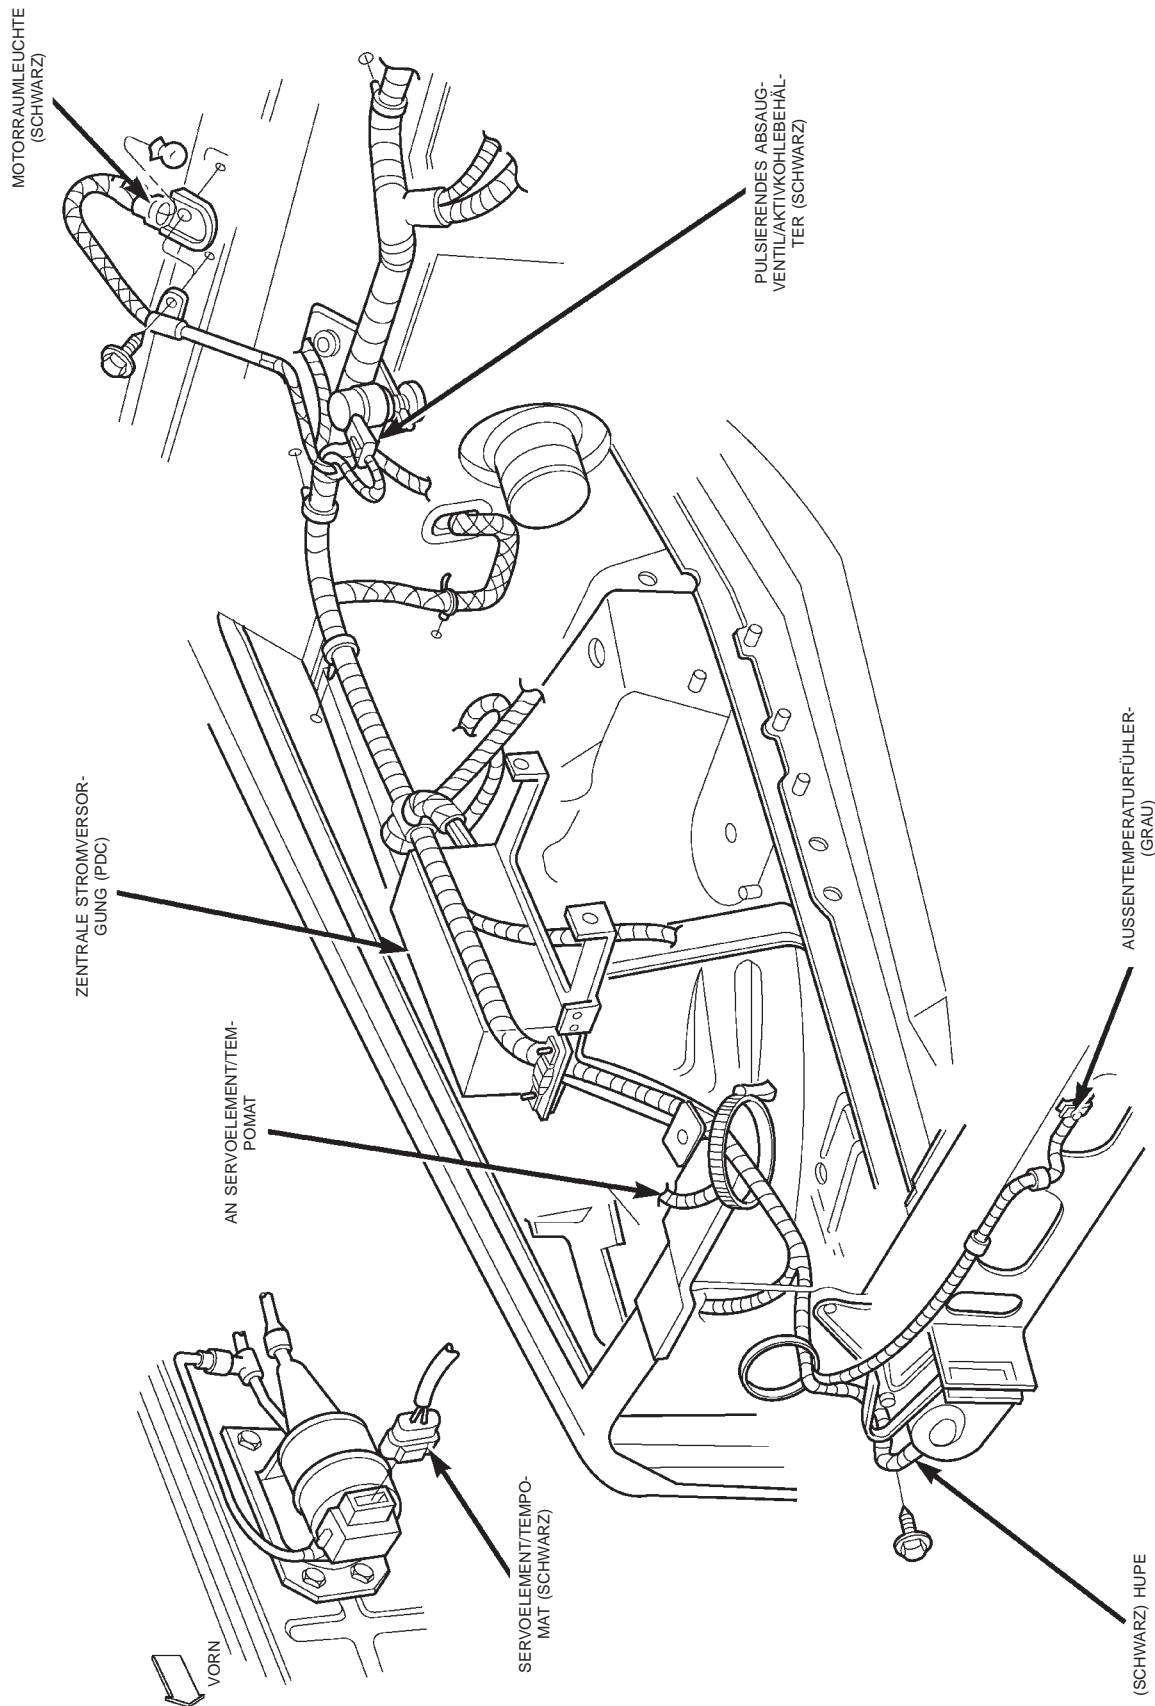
Motorraum rechts 2.5L-Motor Linkslenker
